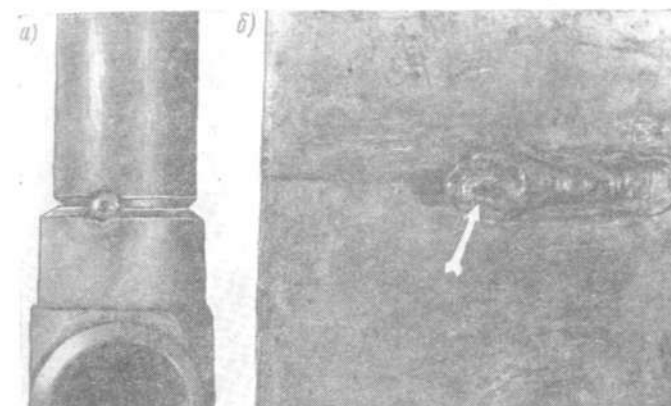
Неправильно выполненная заделка кратера на прихватках: а — ручная аргано-дуговая сварка; б — ручная дуговая сварка.
